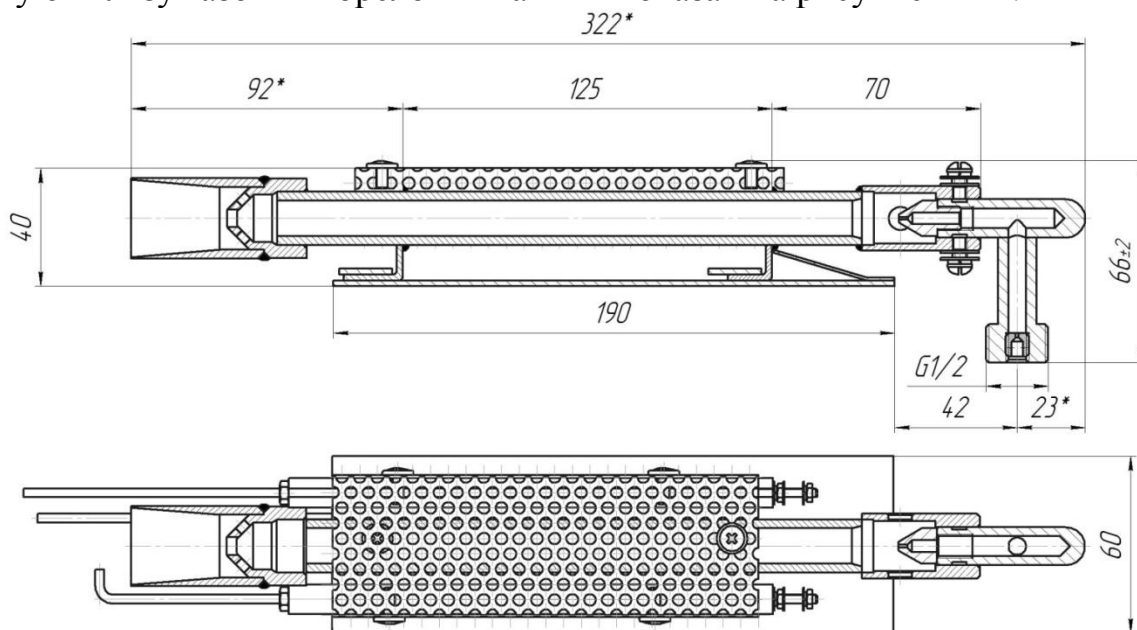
Габаритные и присоединительные размеры горелки ПГ-28М:
